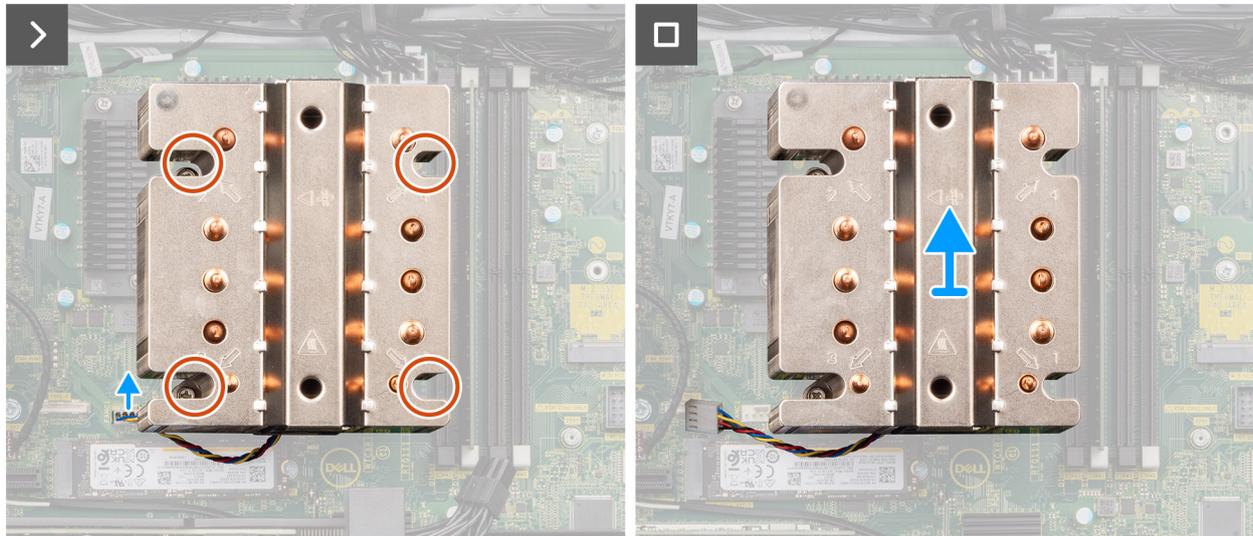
Entfernen des Prozessorlüfters und der 125-W-Kühlkörperbaugruppe
